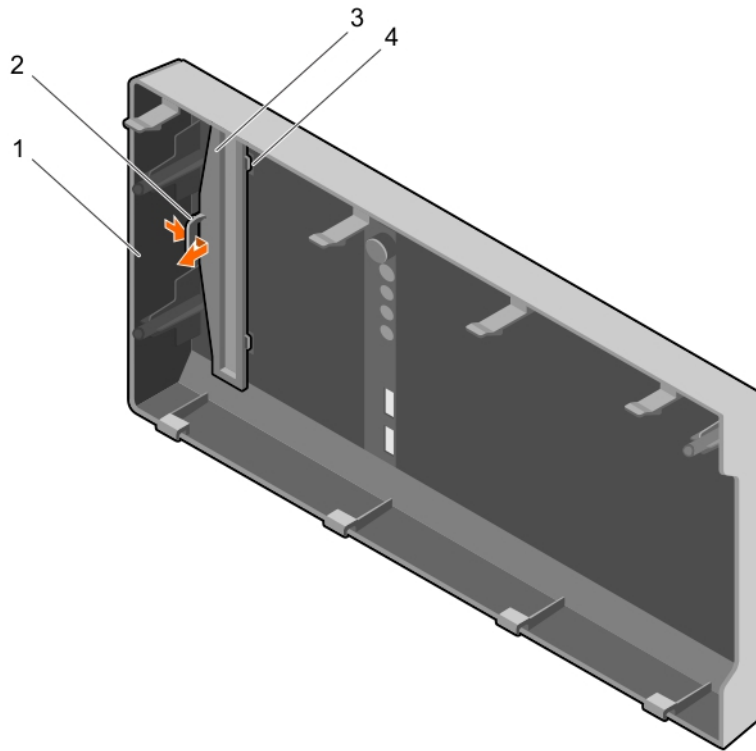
Entfernen des Platzhalters für das optische Laufwerk aus der Blende
